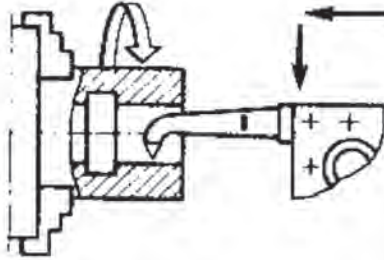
Доторк вершини головки різьбового різця поверхні отвору заготовки
